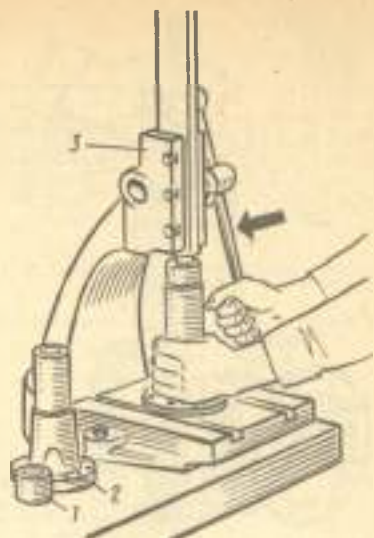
Запрессовка втулки в ступицу рулевого колеса:
